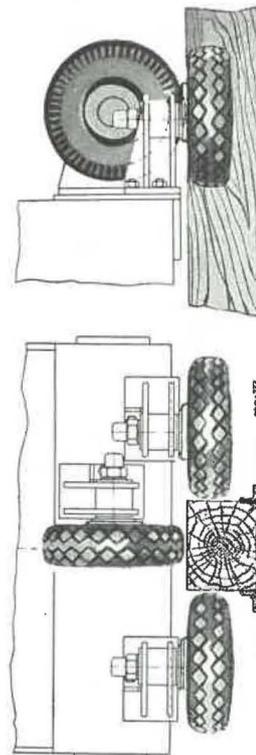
Galets de guidage Demag avec pneus à gonfler pour cages et pour skip.
